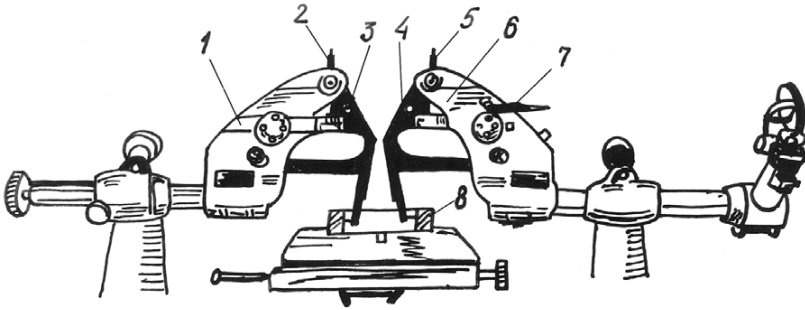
Пристосування для внутрішніх вимірювань: 1 – ліва державка; 2 – гвинт кріплення дуги пінолі; 3, 4 – вимірювання дуги; 5 – гвинт кріплення дуги; трубки оптиметра; 6 – перша державка; 7 – аретир; 8 – деталь (виріб).
